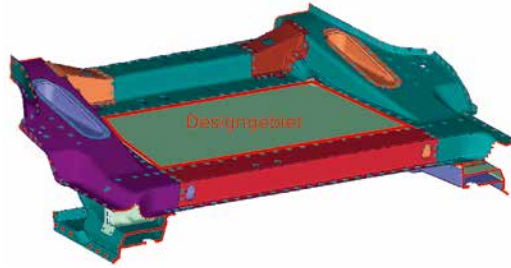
Hier eine Optimierungsaufgabe bei einer Fahrzeugbodengruppe der Adam Opel AG (links).
